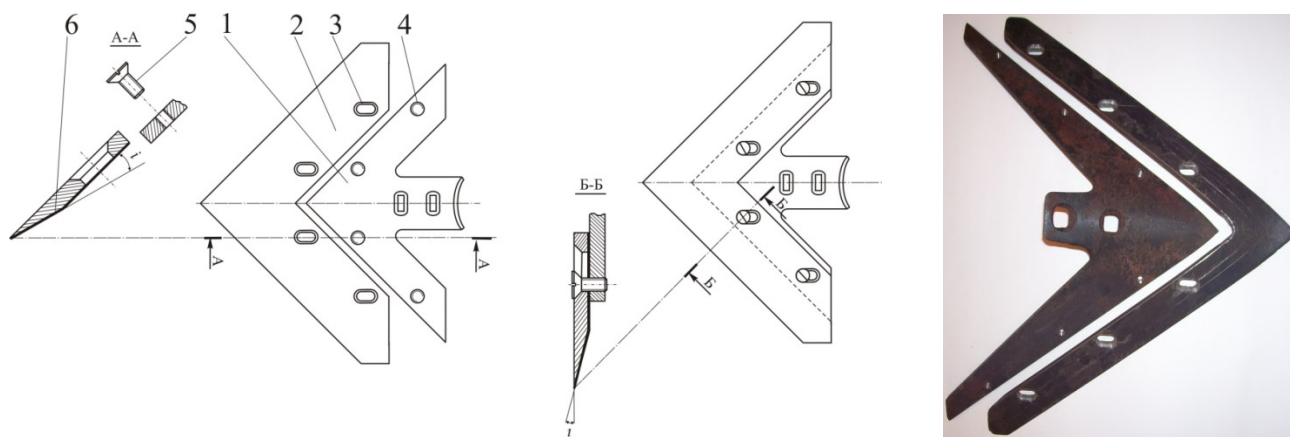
Схема восстановления, стрелчатой лапы культиватора постановкой ремонтной детали: 1 – остов стрелчатой лапы; 2 – сменная режущая часть (компенсирующая деталь); 3 – крепежные отверстия; 4 – резьбовые отверстия; 5 – винты; 6 – одно- или двустороннее упрочняющее покрытие
